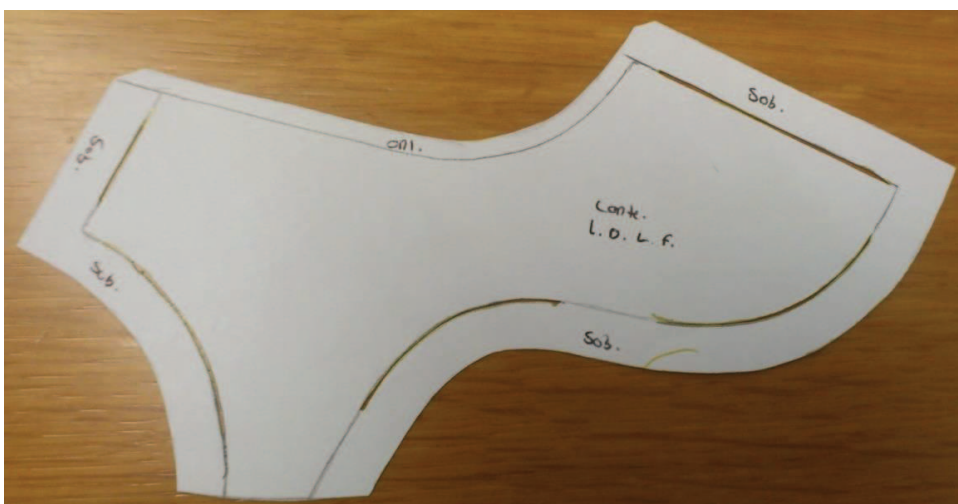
Plano de corte laterais (Molde dentro e fora)
